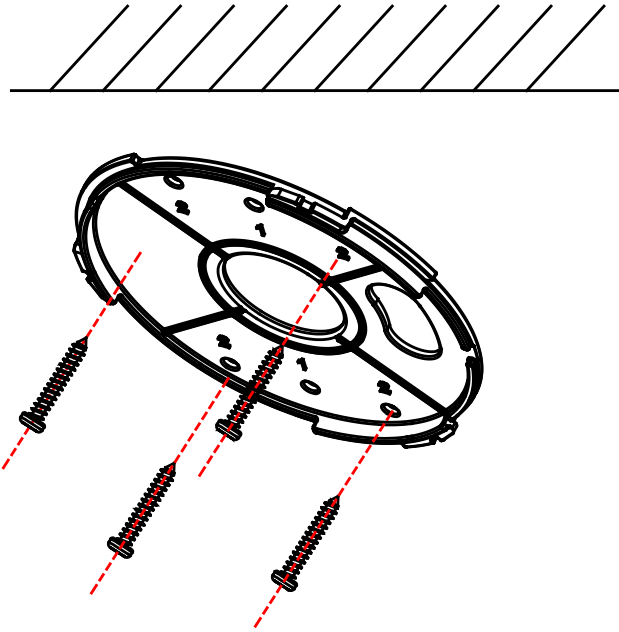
Крепление монтажного основания видеокамеры на потолок / стену
